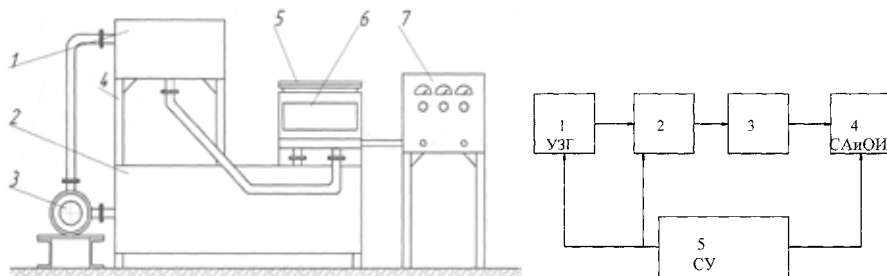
Схема ультразвуковой установки для снятия внутренних остаточных напряжений: 1 – верхний бак, 2 – нижний бак, 3 – насос, 4 – стойка, 5 – коленчатый вал, 6 – рабочая ёмкость, 7 – генератор ультразвуковой
